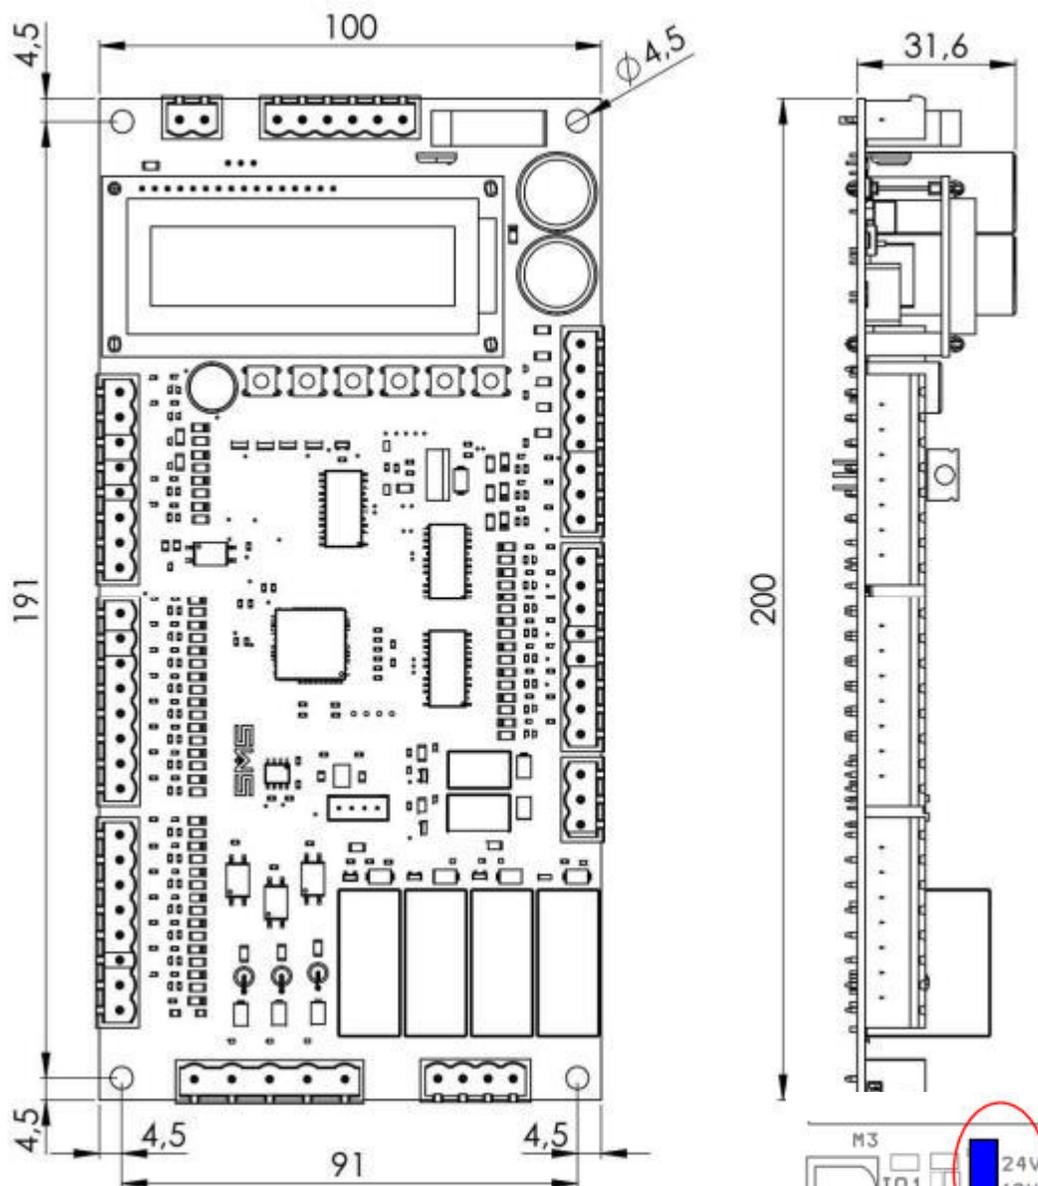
Esquema y dimensiones de la placa de control y componentes
